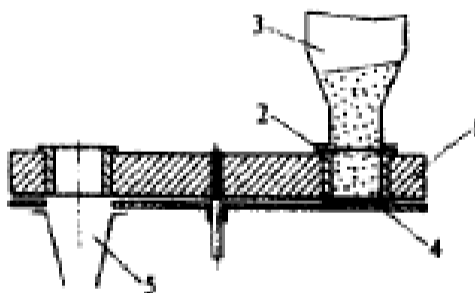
Порційний дисковий дозатор з мірними циліндрами
